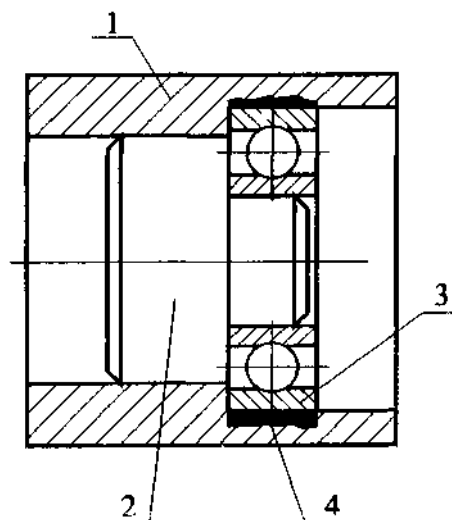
Восстановление поверхности неразъемного гнезда подшипника с использованием специального центрирующего приспособления; 1 корпус, 2 центрирующее приспособление; 3 - подшипник; 4 - металлополимерный материал.
